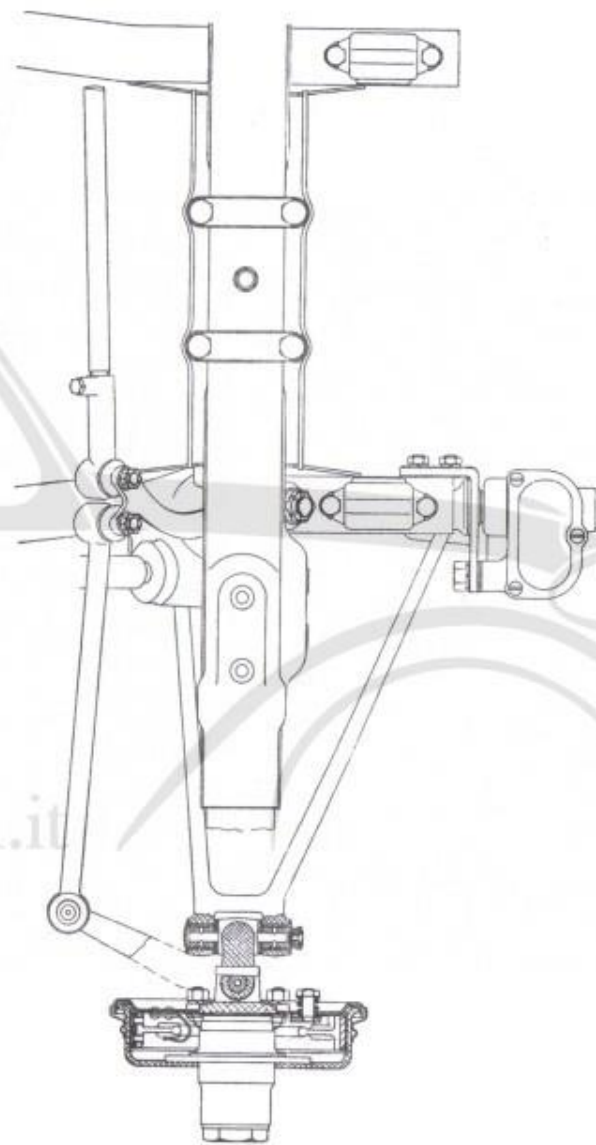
Sospensione anteriore vista in pianta con sezione sul freno e sul perno del montante.
